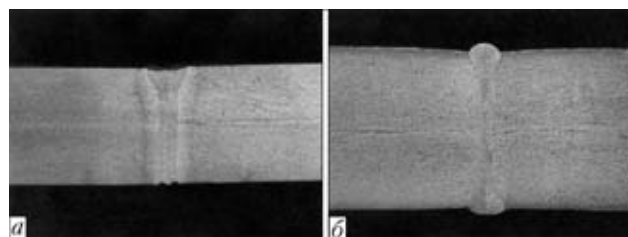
Примеры использования оптоволоконного лазера мощностью 6,9 м/мин для сварки стыкового шва на стали 1.4301: а — макрошлиф соединения толщиной 5 мм, скорость сварки 4 м/мин, один проход; б — макрошлиф соединения толщиной 10 мм, скорость сварки 3 м/мин, сварка двухсторонняя
